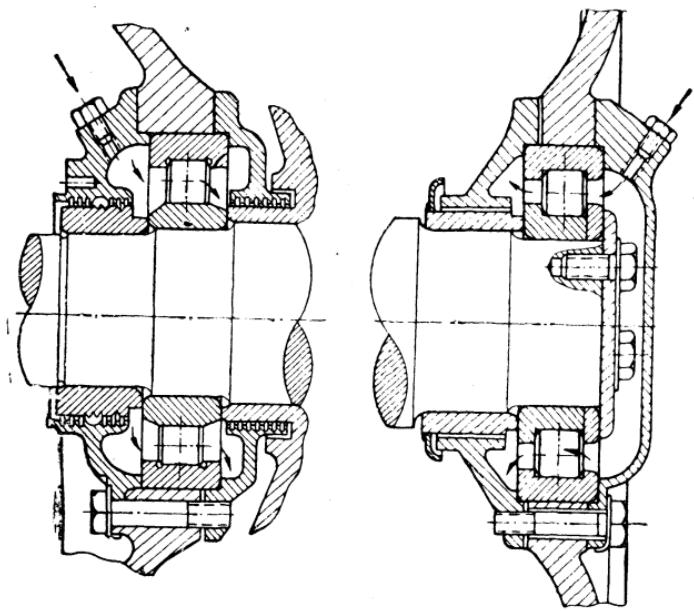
Смазка якорных подшипников мотор-генератора НБ-429
